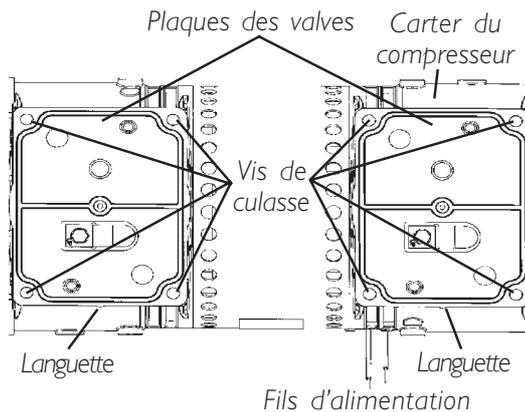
DEMONTAGE DU COMPRESSEUR ET DE LA CULASSE DU COMPRESSEUR
